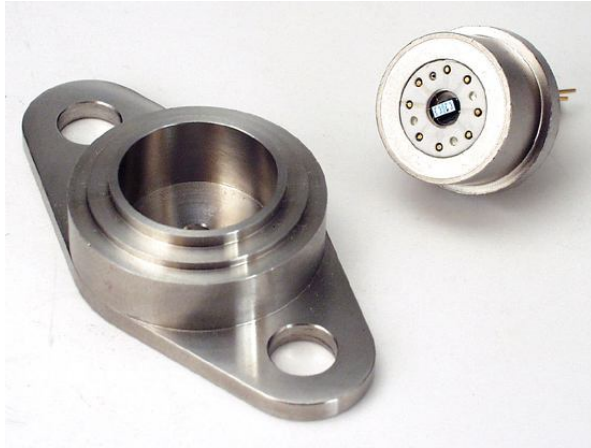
Чувствительный элемент датчика давления и деталь корпуса, в которую он монтируется
